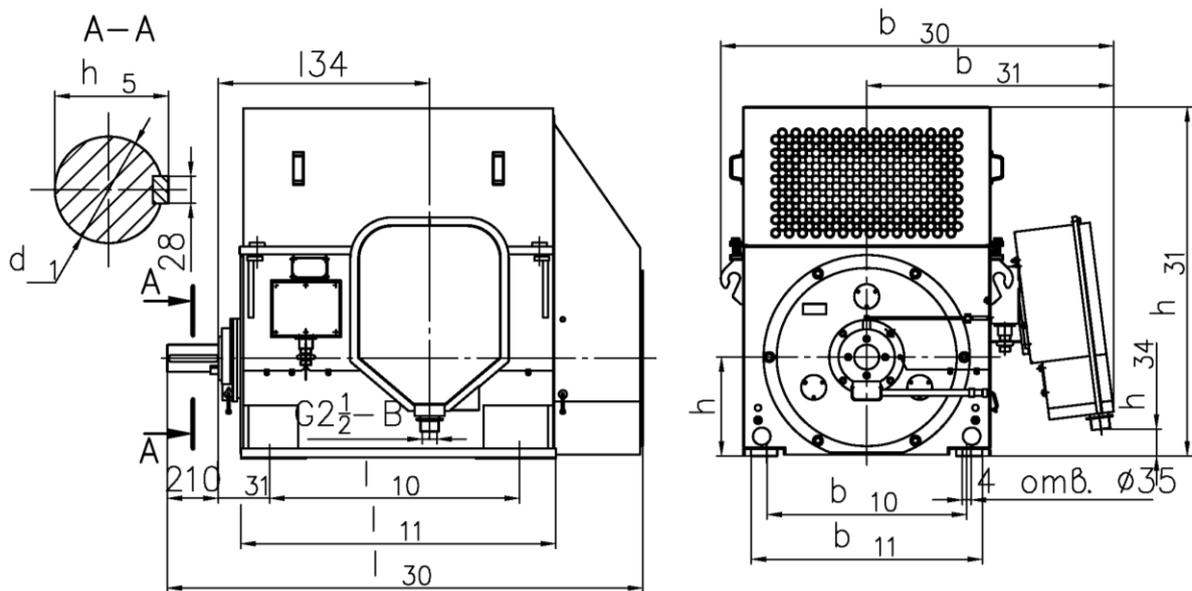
Электродвигатели серии ДАЗО со сварной коробкой
